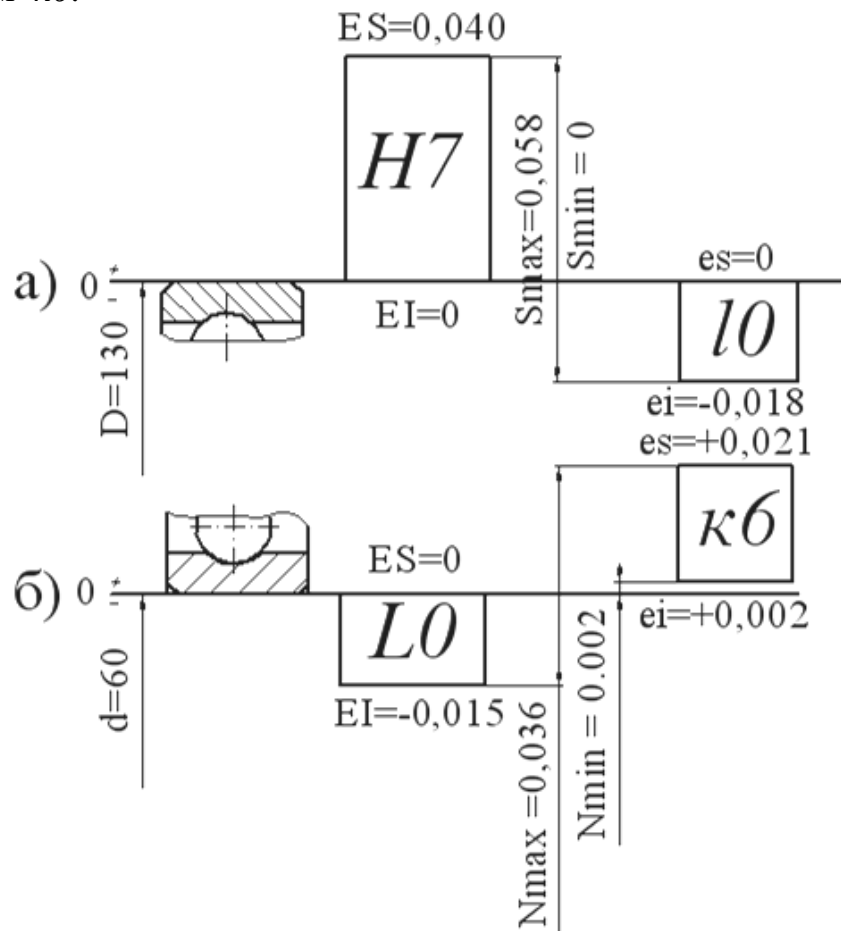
Схема расположения полей допусков сопряжений: а) «наружное кольцо – корпус» б) «внутреннее кольцо – вал».
